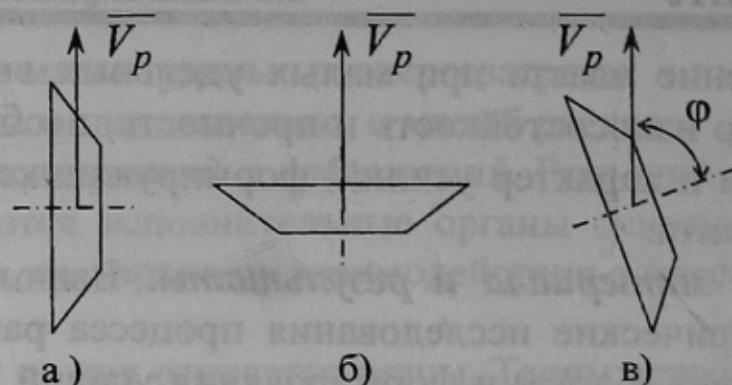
Схемы установки режущего инструмента с вращающейся режущей кромкой.
